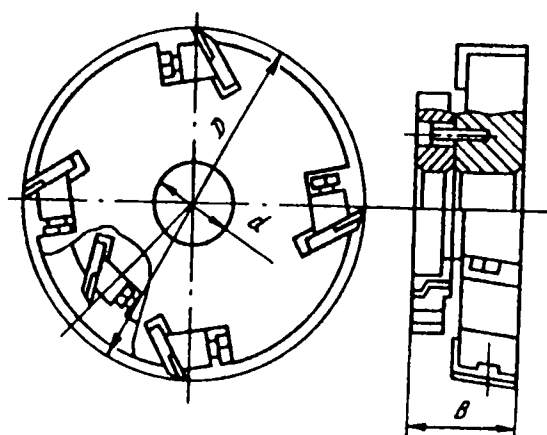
Пример фрезы для обработки окон (для обработки сборочных единиц по периметру)
